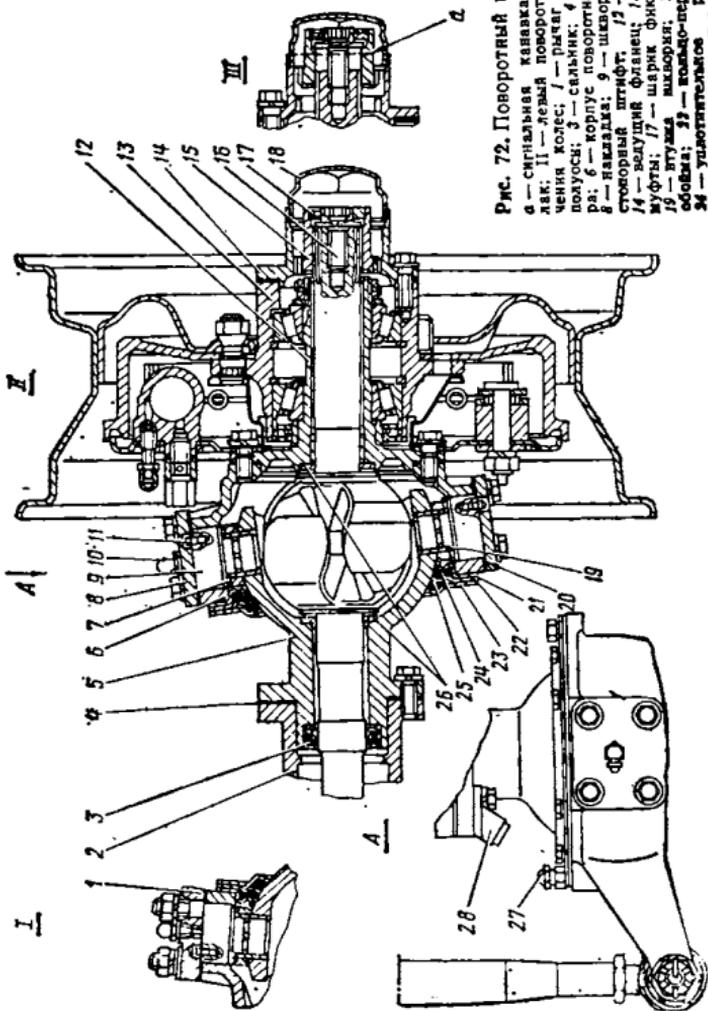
Поворотный кулак автомобиля УАЗ-469Б:
